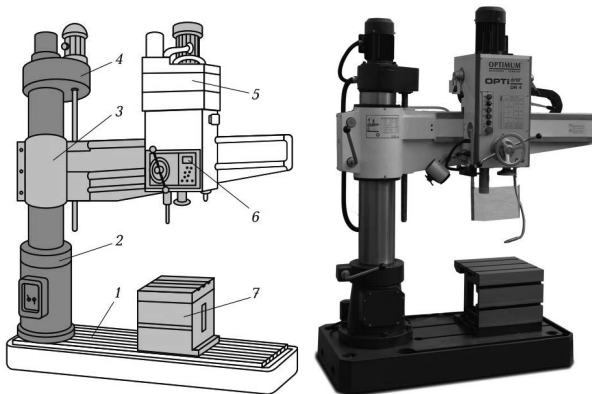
Радіально-свердильний верстат: 1 – фундаментна плита; 2 – цоколь; 3 – рукав; 4 – механізм підйому; 5 – шпиндельна головка; 6 – пульт управління; 7 – стіл
